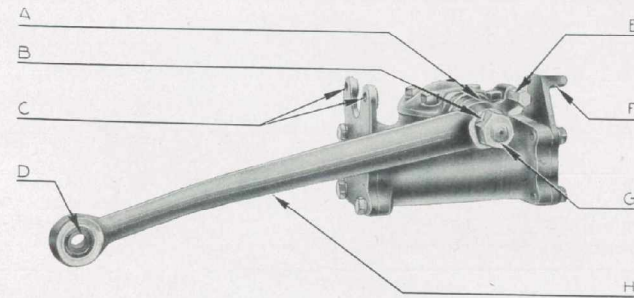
HYDRAULISCHER STOSSDÄMPFER
